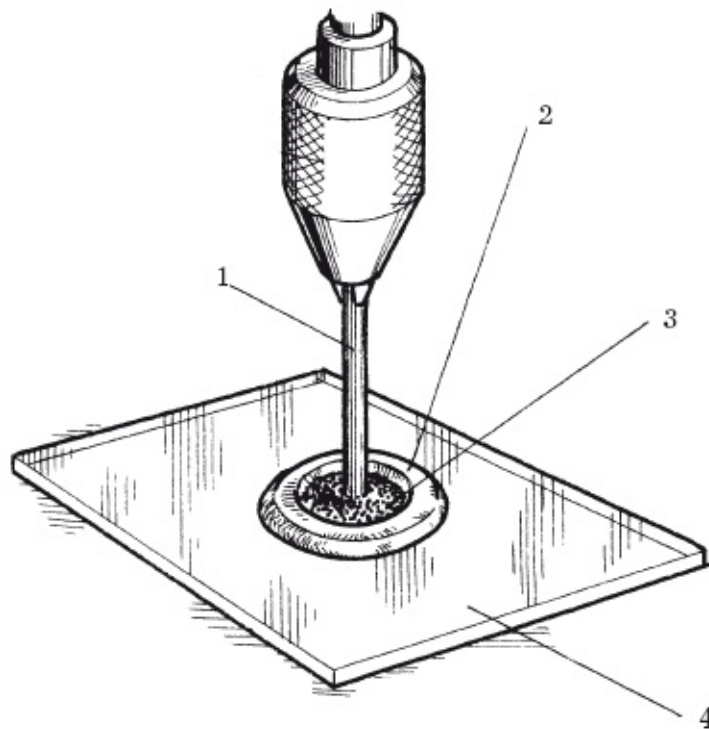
Сверление стекла с помощью медной трубки: 1 – медная трубка; 2 – пластилин; 3 – корундовый порошок; 4 – стекло
